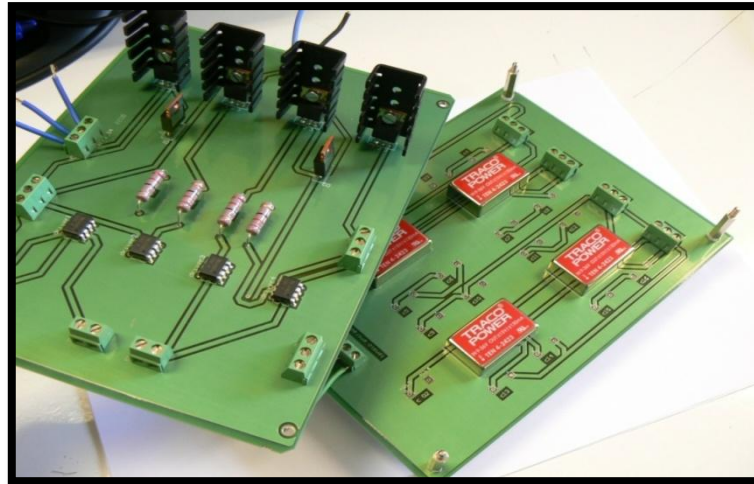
Plaques PCB muntades amb tots els seus components.
